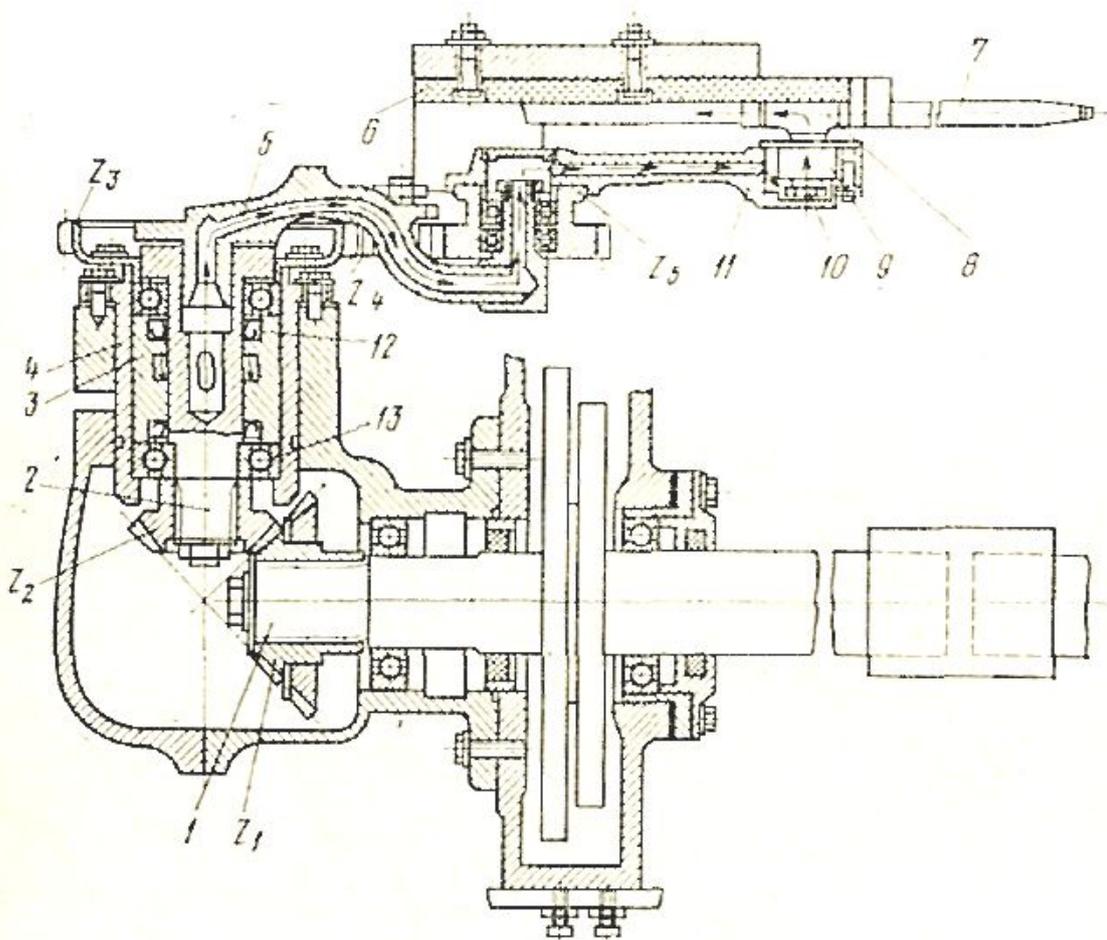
Рапирный механизм: 1- главный вал станка, 2- вертикальный вал, 3- распорная втулка, 4- стакан для радиальных шарикоподшипников, 5- водило, 6- направляющая, 7- рапира, 8- форсунка рапиры, 9- стакан, 10- гайки, 11- шатун, 12- уплотнительное кольцо, 13- шарикоподшипник.
